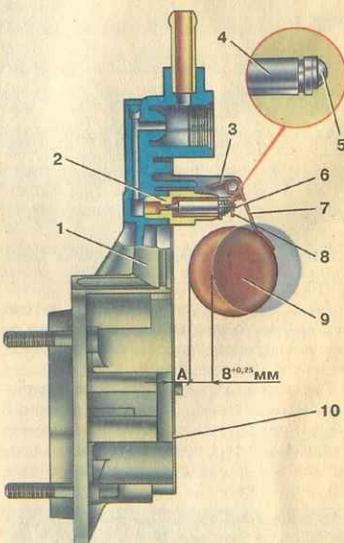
Схема установки уровня топлива в по-плавковой камере: 1 — крышка карбюратора; 2 — седло игольчатого клапана; 3 — упор; 4 — игольчатый клапан; 5 — шарик игольчатого клапана; 6 — оттяжная вилка игольчатого клапана; 7 — кронштейн поплавка; 8 — язычок; 9 — поплавок; 10 — прокладка
